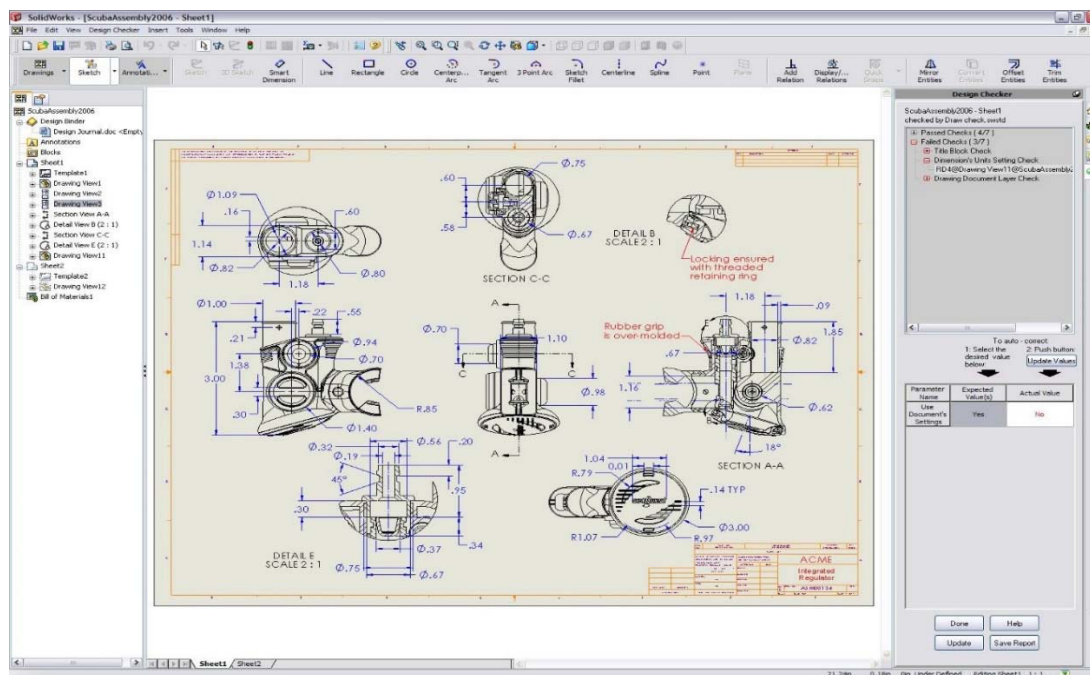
Prüfbericht von Solidworks Design Checker⁸
